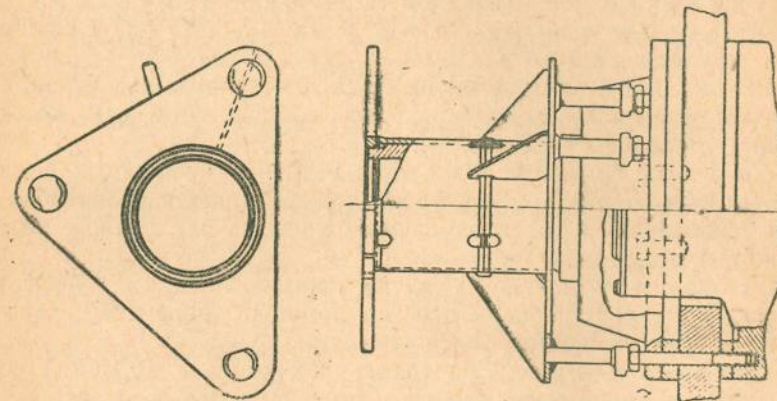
Отжатие бортового редуктора от привалочной плоскости при помощи приспособления № 119
